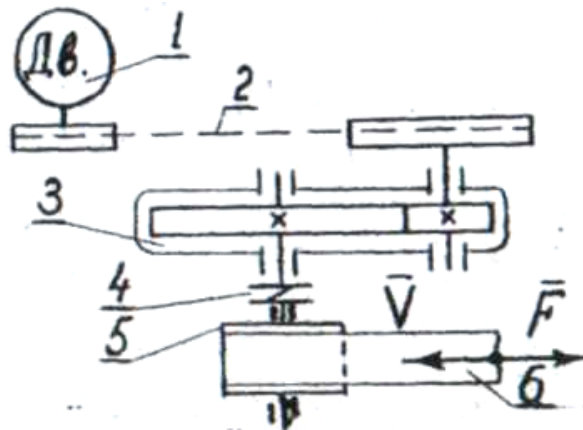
Схема приводу: 1- електродвигун; 2 - пасова передача; 3 – редуктор; 4 – муфта; 5 – барабан; 6 – стрічка
